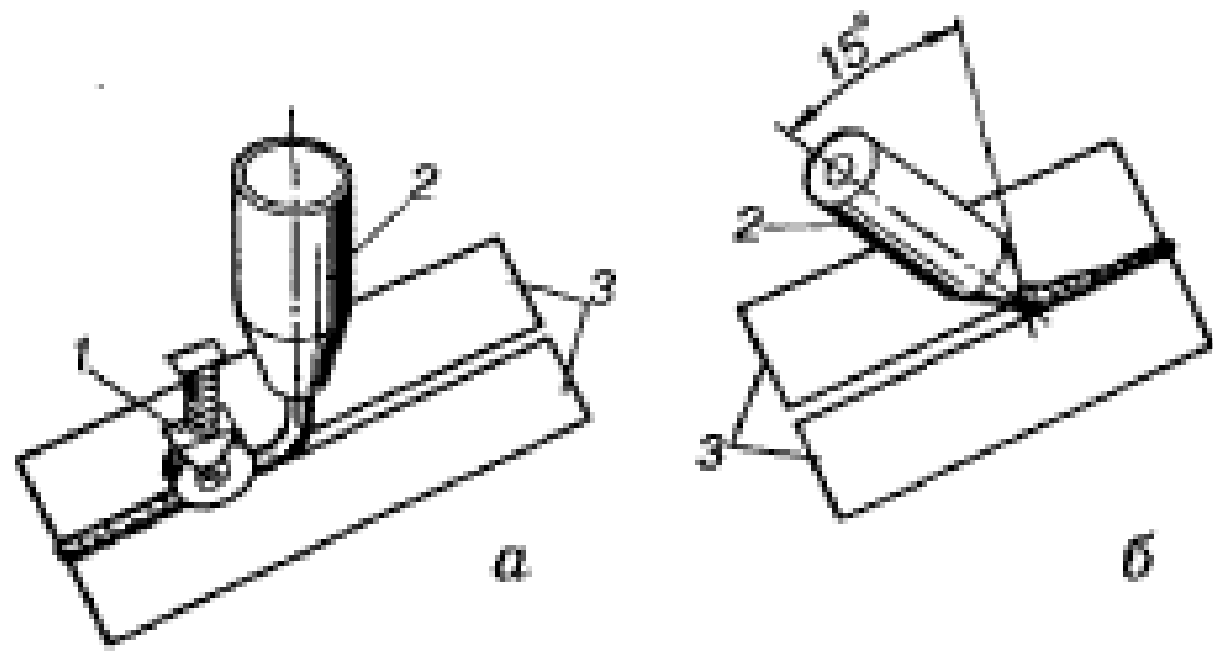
Схеми безконтактного та контактнo-екструзійного зварювання
